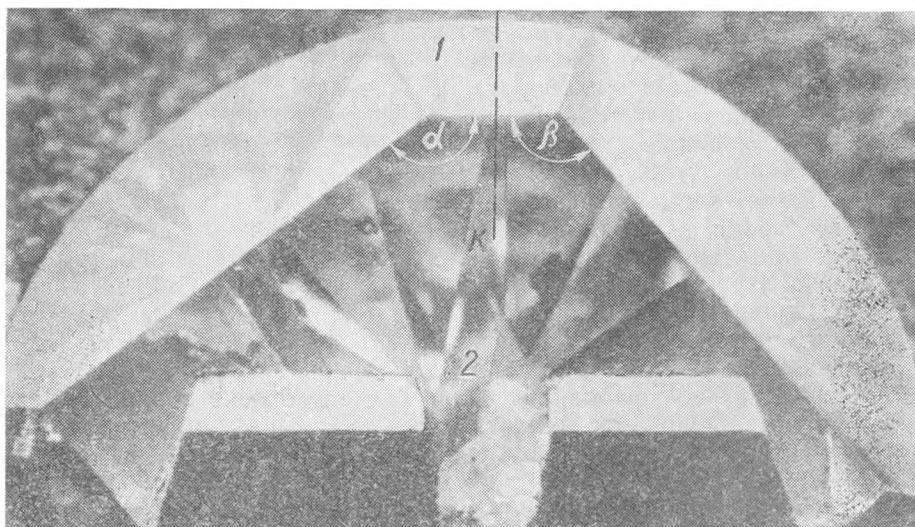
Неправильное расположение первой угловой грани верха (перекос):
